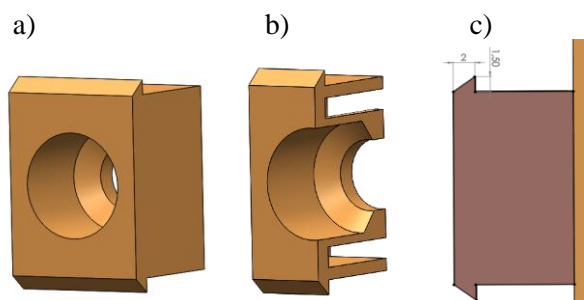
Fixador final: a) fixador, b) vista em corte do fixador; c) cotas do entalhe do fixador.
